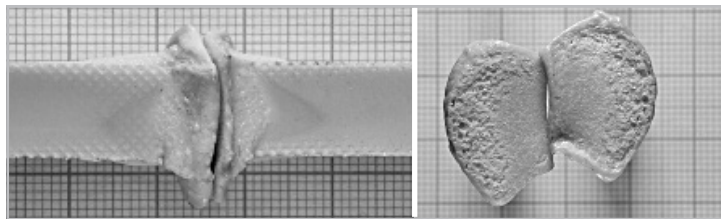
Внешний вид и характер разрушения сварного шва плоских листовых образцов из PEI, полученного при сварке встык с пониженной температурой нагретого инструмента
